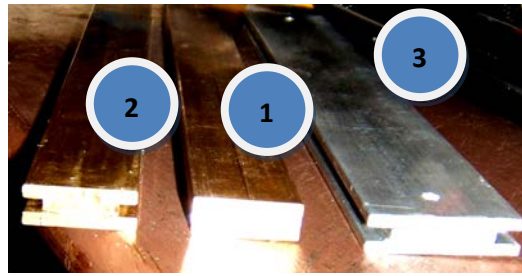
Probetas utilizadas para la prueba de torsión.
